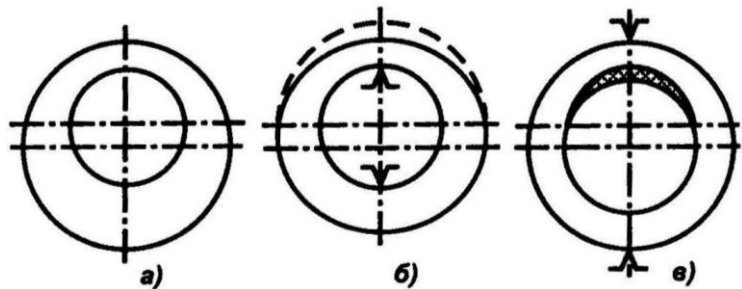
Можливі похибки форми деталей через похибки форми заготовок
